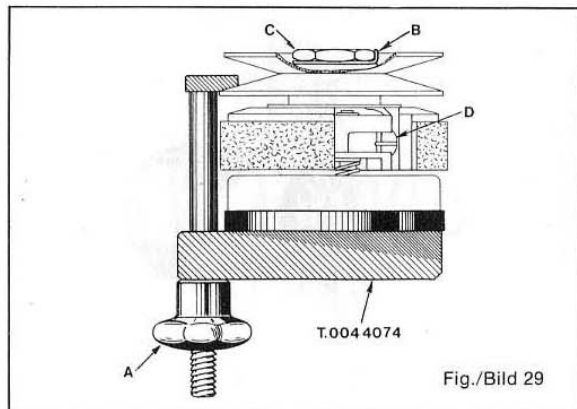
Regelscheibe der angetriebenen Riemen-scheibe: Die Kupplungsgruppe im Gerät T. 0044074 einspannen, die Mutter "A" drehen sodaß die Feder zusammen gedrückt wird, das Sicherungsblech "B" niederbiegen und Mutter "C" ausschrauben, zuletzt Mutter "A" lösen um die Feder langsam zu entladen. Die drei Rückzugfedern "D" werden mit einem Schraubenzieher ausgehebelt, dann können die Fliehkraftgewichte herausgenommen werden.
